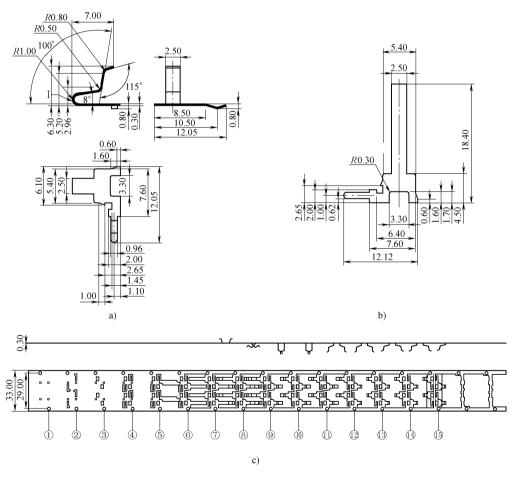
弹片级进模 a) 零件图 b) 展开图 c) 排样图
